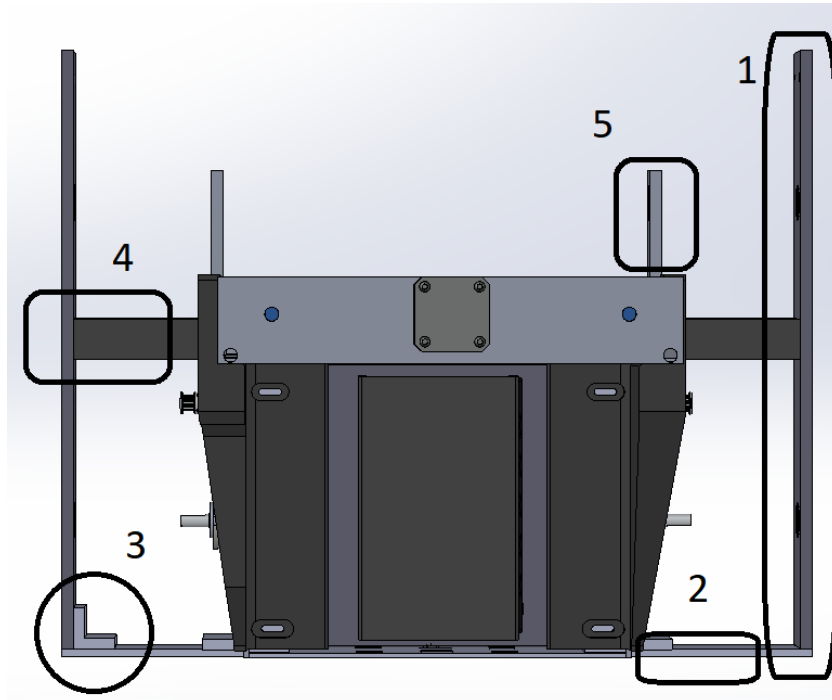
Estructura mecanismo elevador, vista isometrica.
